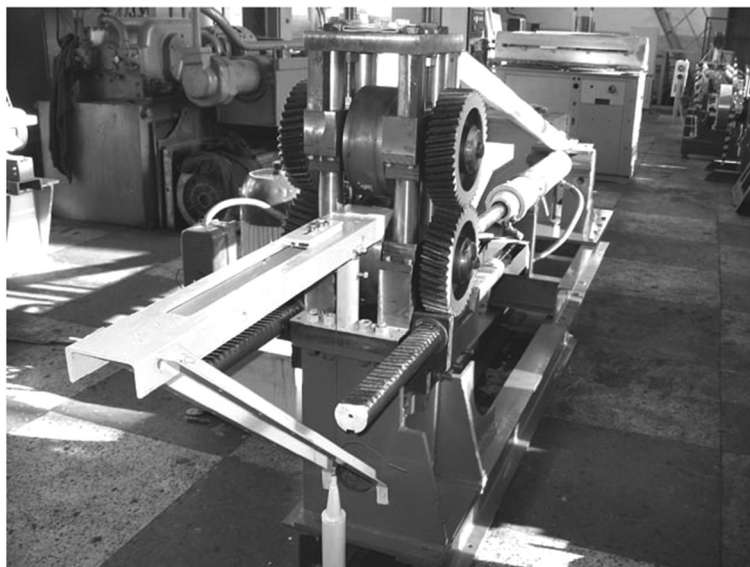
Экспериментальный стан для прокатки заготовок защитных элементов корпусов плугов
